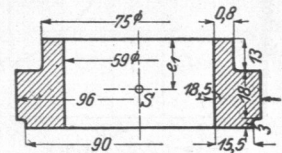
Querschnitt FB des Flansches Abb. 669.
